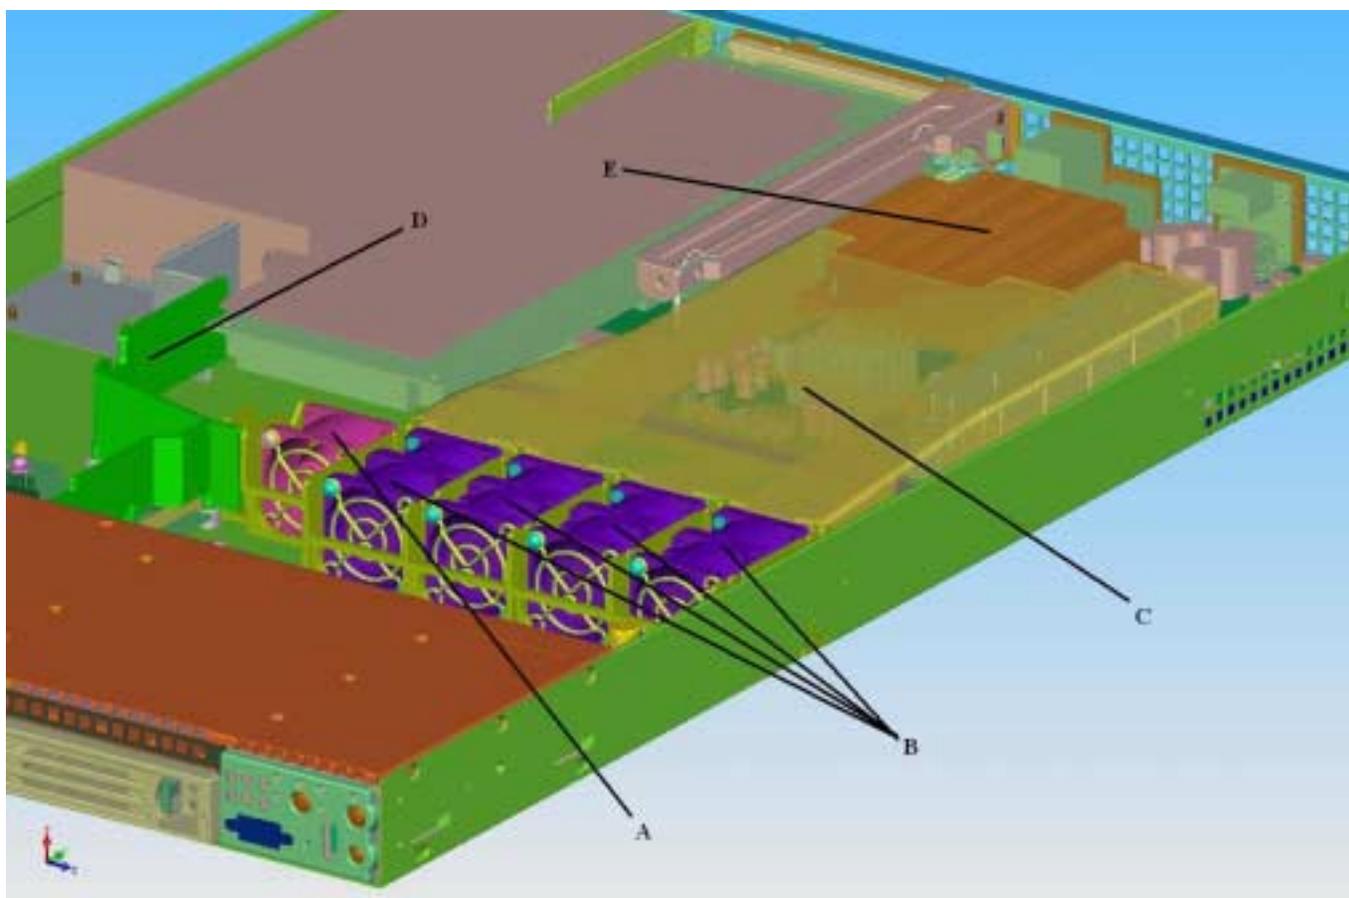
Подсистема охлаждения серверного корпуса Intel® SC1400UP
